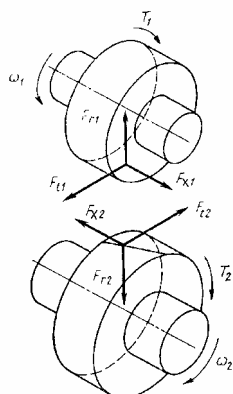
Силы, действующие в зацепление цилиндрической косозубой передачи
